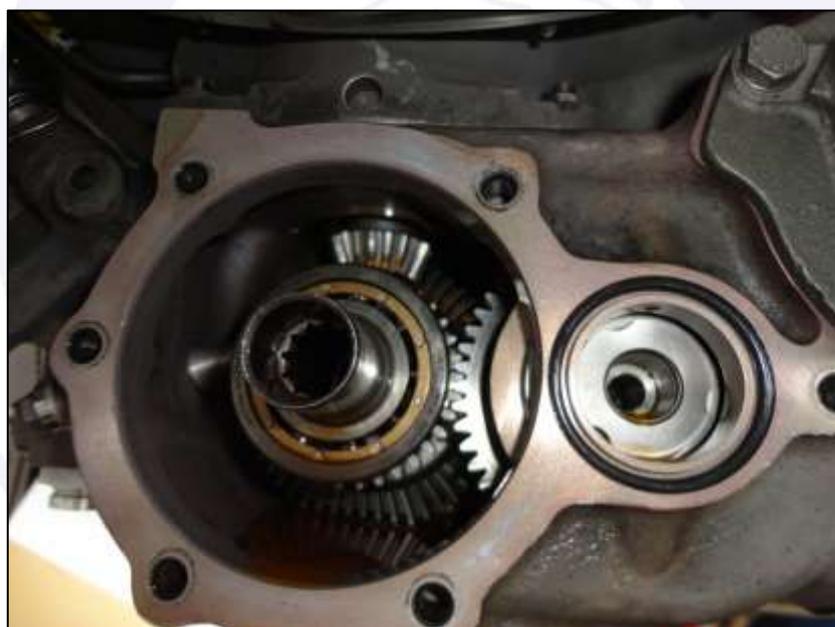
Local de acoplamento do starter-generator na gearbox, em destaque.
